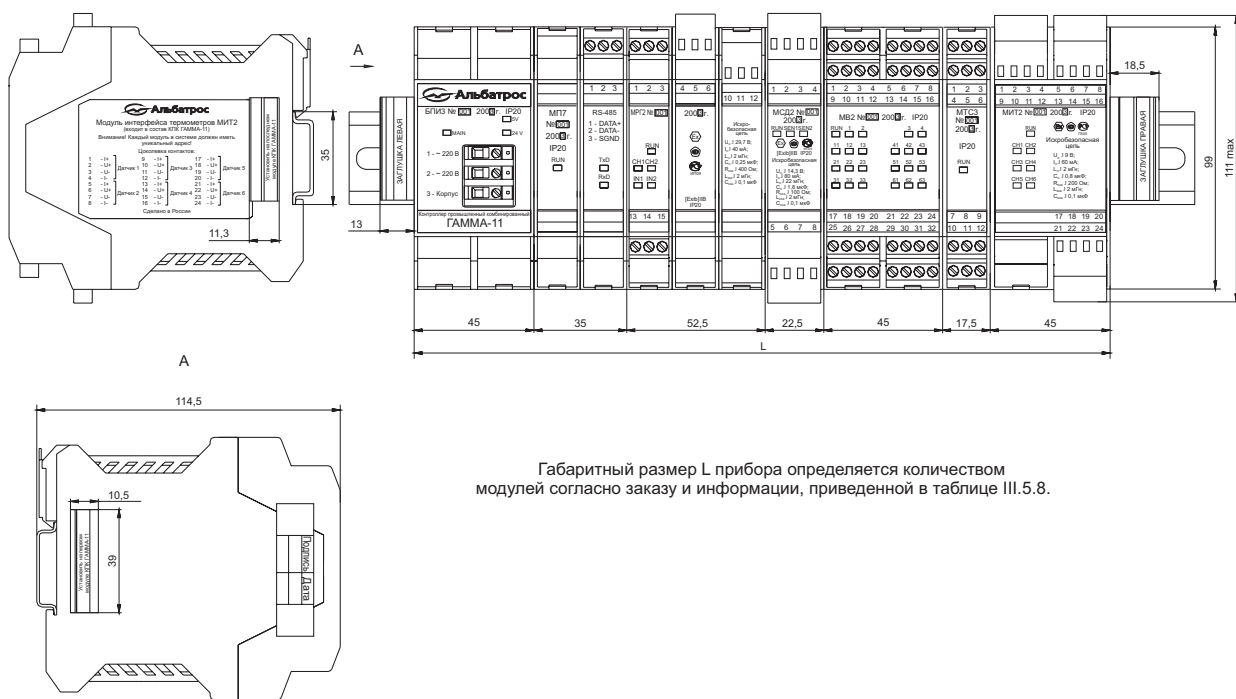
Внешний вид и габаритные размеры составных частей прибора (вариант установки на один DIN-рельс)
